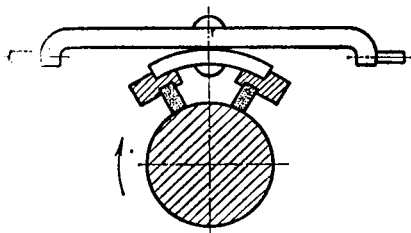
Доводка цилиндрических поверхностей колеблющимися брусками
